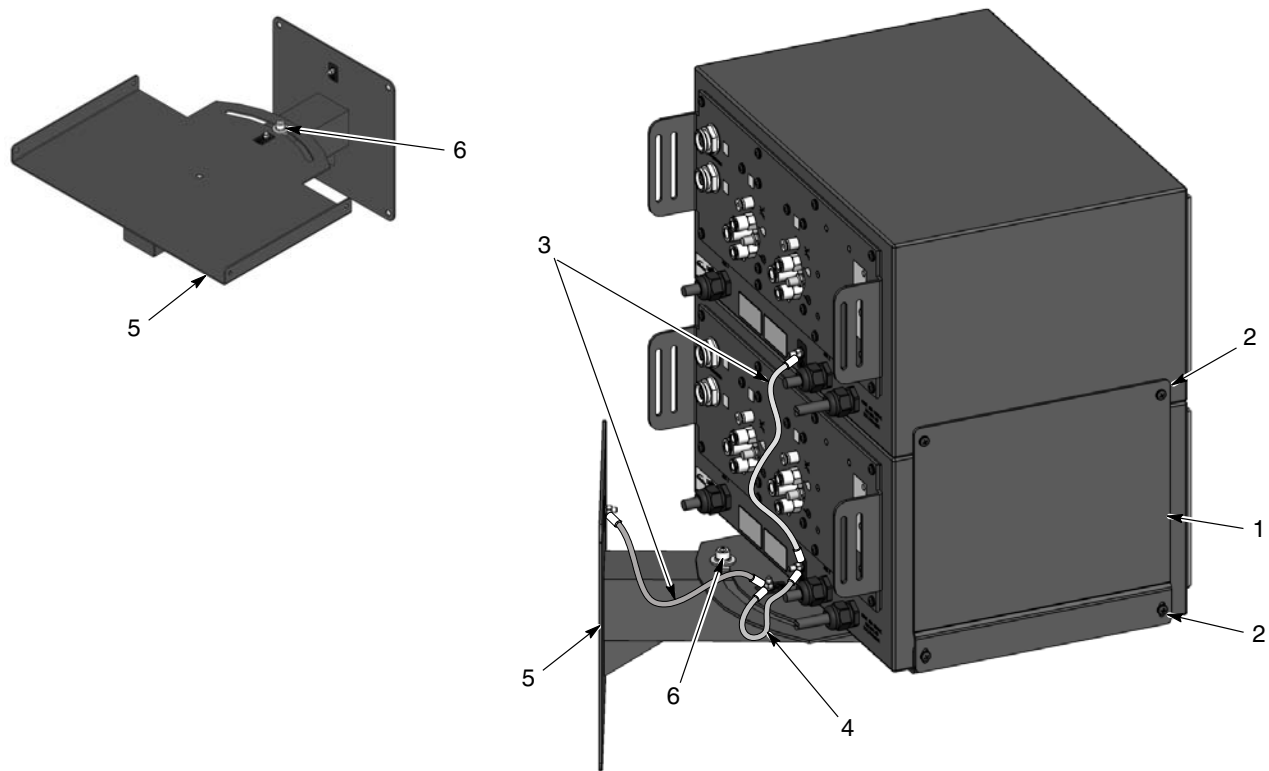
Montage einer Doppelpistolensteuerung mit optionaler Wandmontagehalterung
